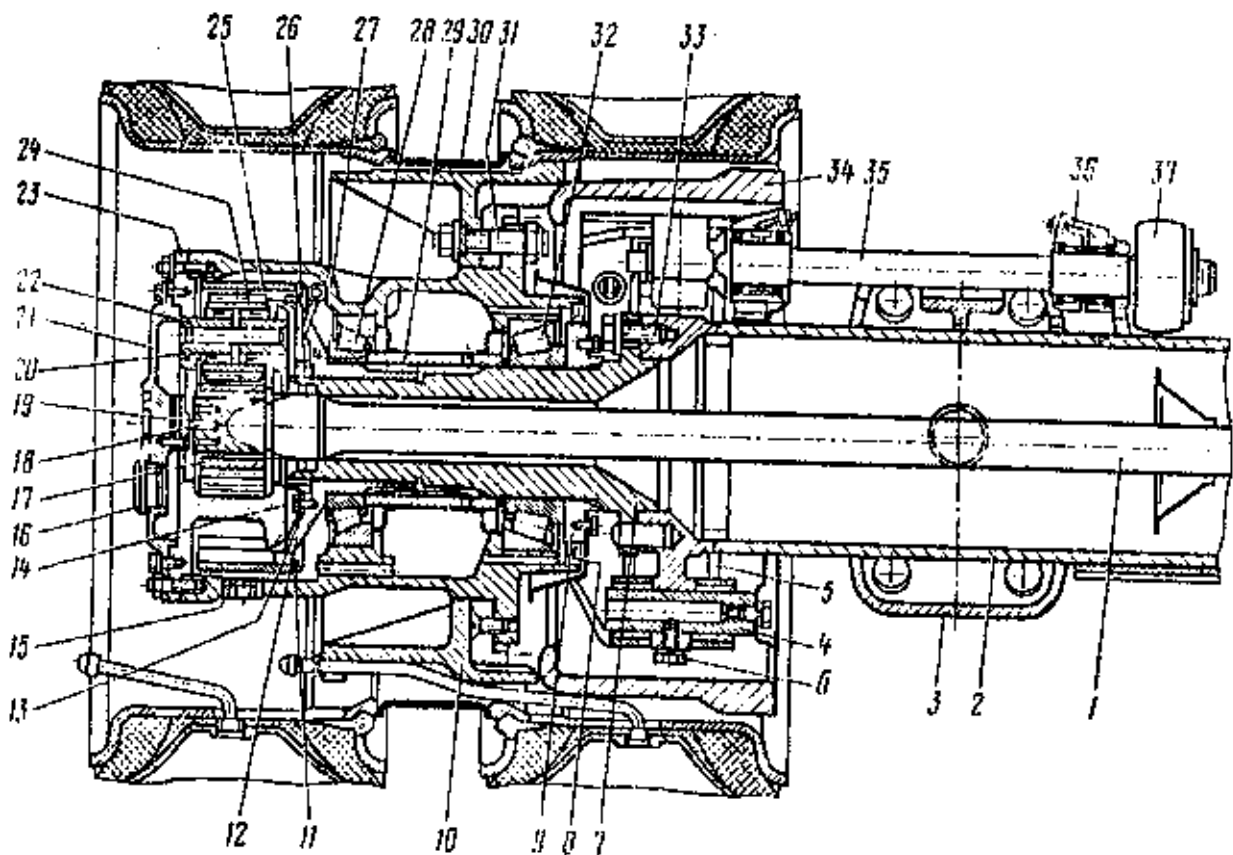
Маточина колеса і колісний редуктор ведучого моста:
